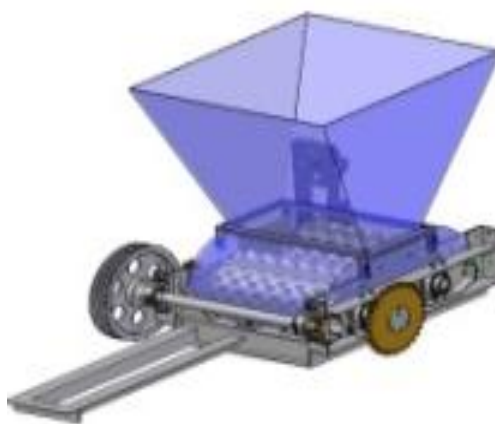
Diseño Molino de rodillos de Carbón. Fuente: Hojas de vida equipos Coquecol SA Cl.
